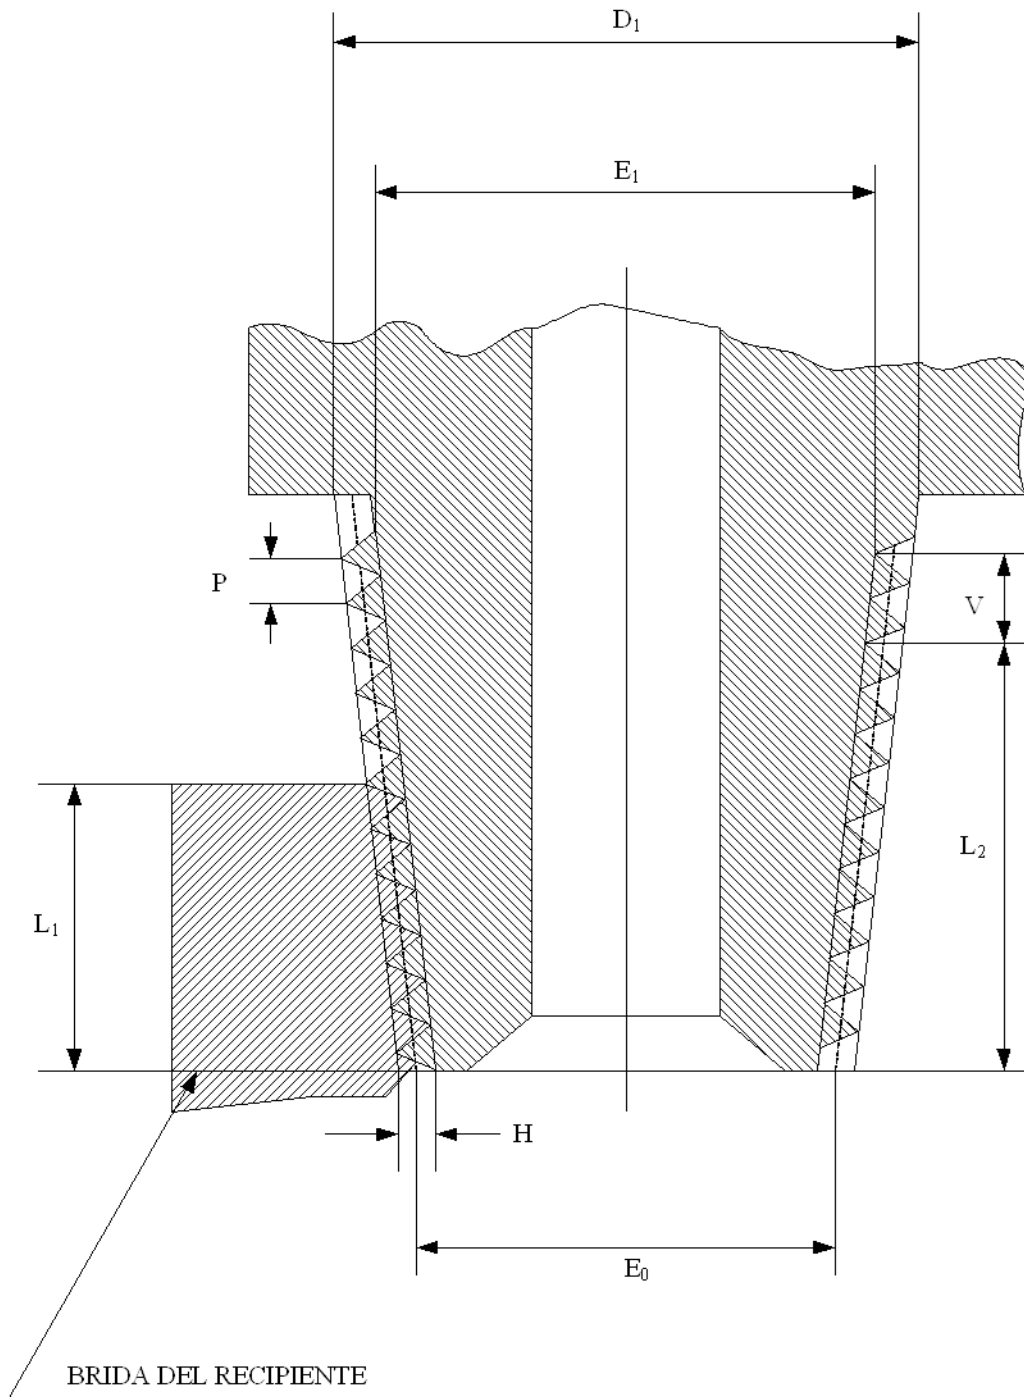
Dimensiones de roscado externo cónico de la válvula.
